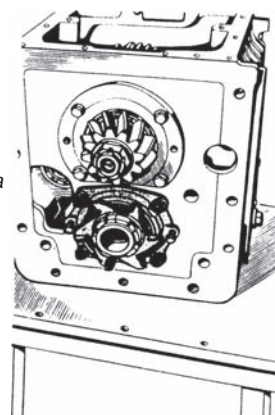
Выпрессовка стакана ведущей шестерни II ступени редуктора в сборе, снятие крыльчатки (открутить четыре болта крепления стакана, выпрессовать стакан).
